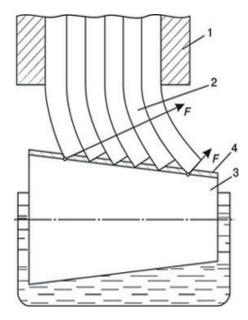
Схема заклейки блоков коническими роликами после фрезерования корешка: 1 - зажим; 2- тетради блока; 3 - конический ролик; 4 -клеевой слой; F - сила, действующая на тетрадь
